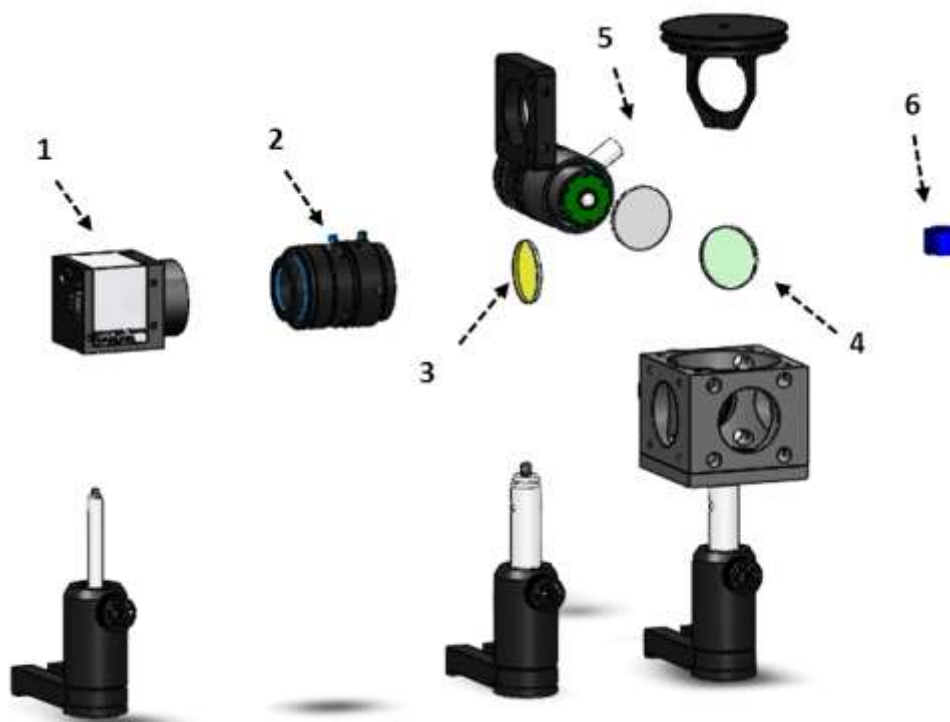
Vista explodida da montagem óptica montada em bancada – Gerada em SolidWorks®.
